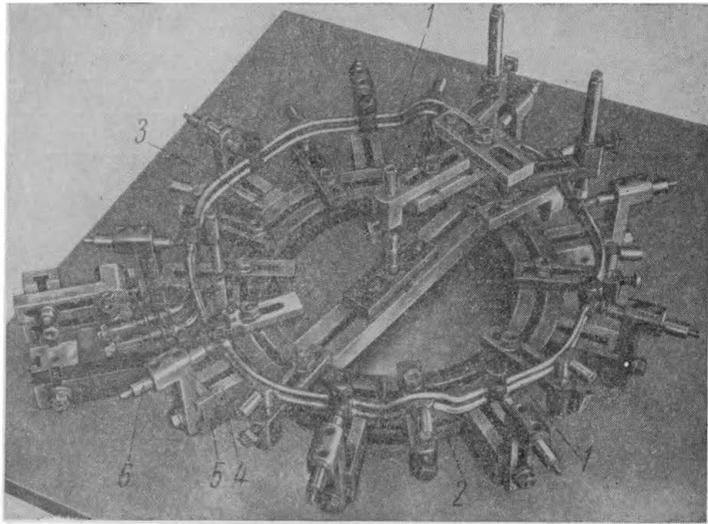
Универсально-сборное приспособление для сборки и прихватки под сварку боковых ребер к корпусу:
